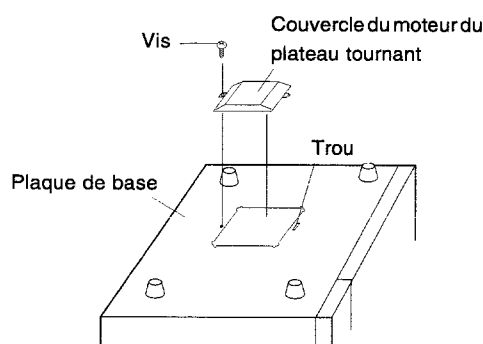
(b). Réinstallation du couvercle du moteur du plateau tournant
